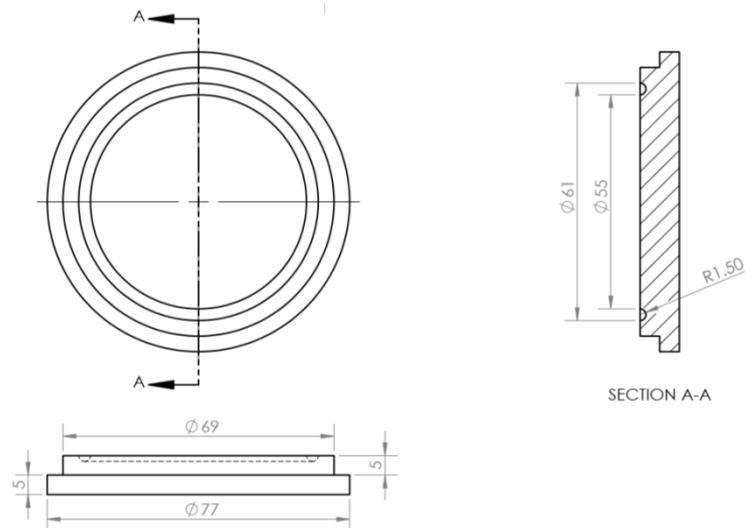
Dimensi plat bawah *mold* tutup dongkrak
